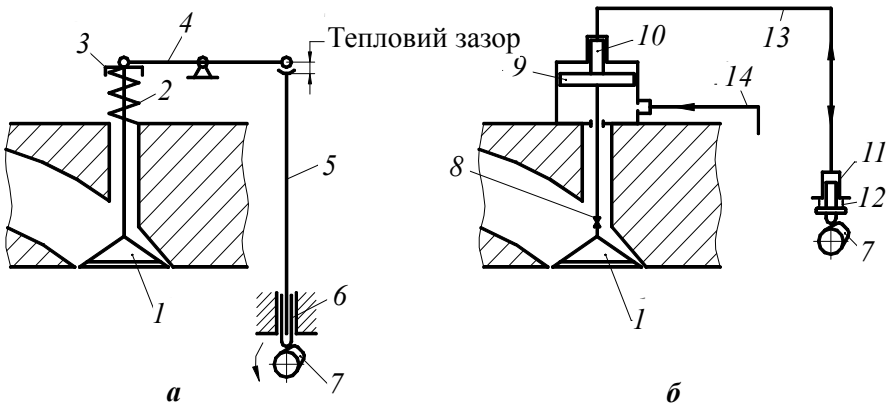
Схеми конструктивного виконання механізмів газорозподілу:
